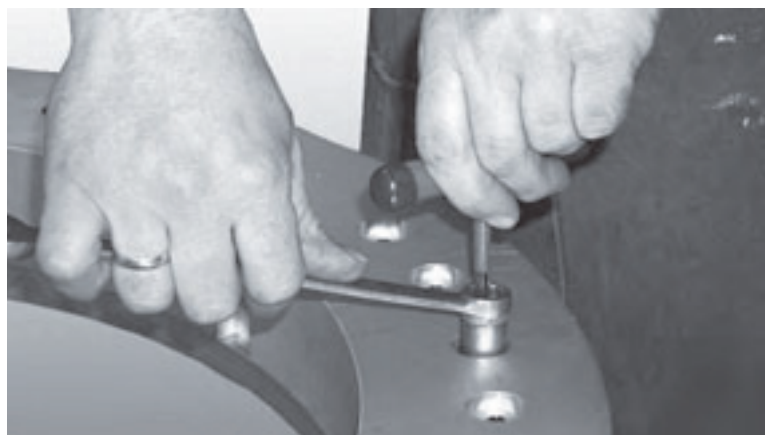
Поверните вал подшипника по часовой стрелке шестигранным ключом и затяните стопорную гайку с нейлоновой вставкой.
